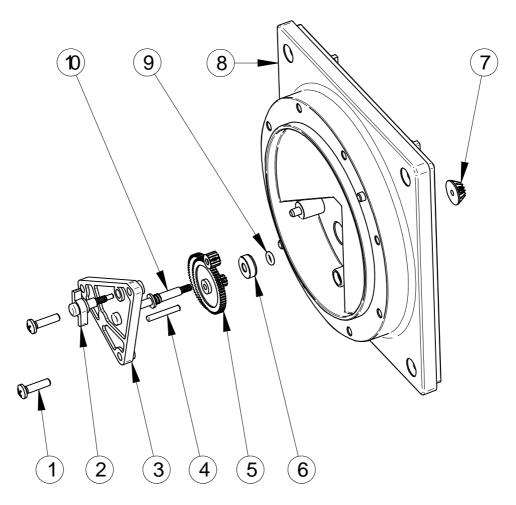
Desenho de explosão da parte inferior da carcaça com engrenagem
